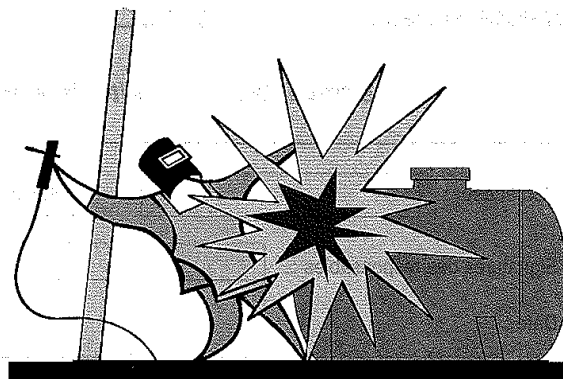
EXPLOSION DUE A UN DEGAZAGE INCOMPLET
